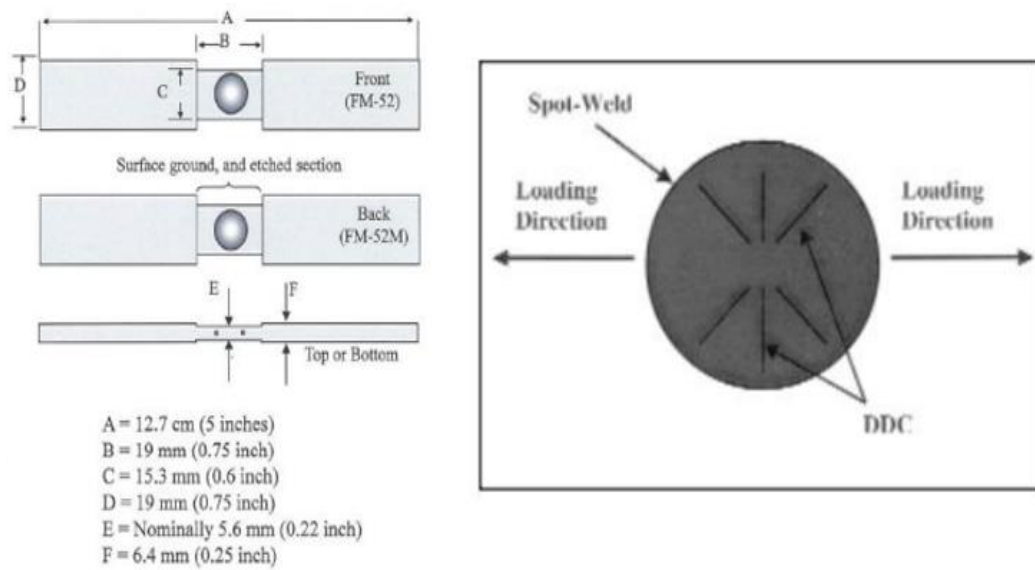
A la izquierda geometría de muestra estándar para el ensayo STF, a la derecha arreglo de granos columnares en el punto de soldadura [11].
